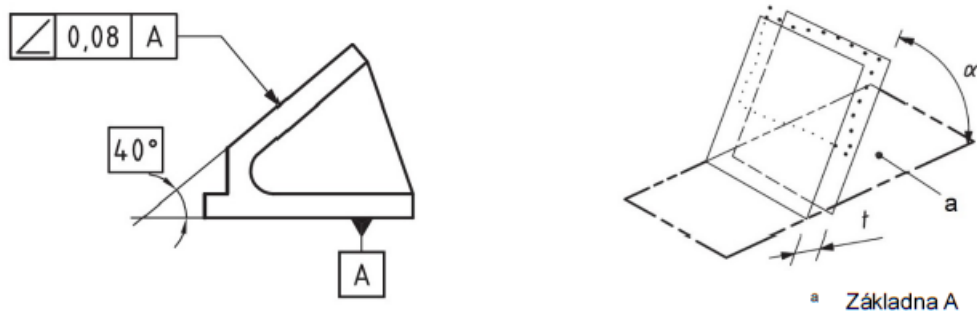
Vymezení tolerančního pole tolerance kolmosti pomocí základny [14]
